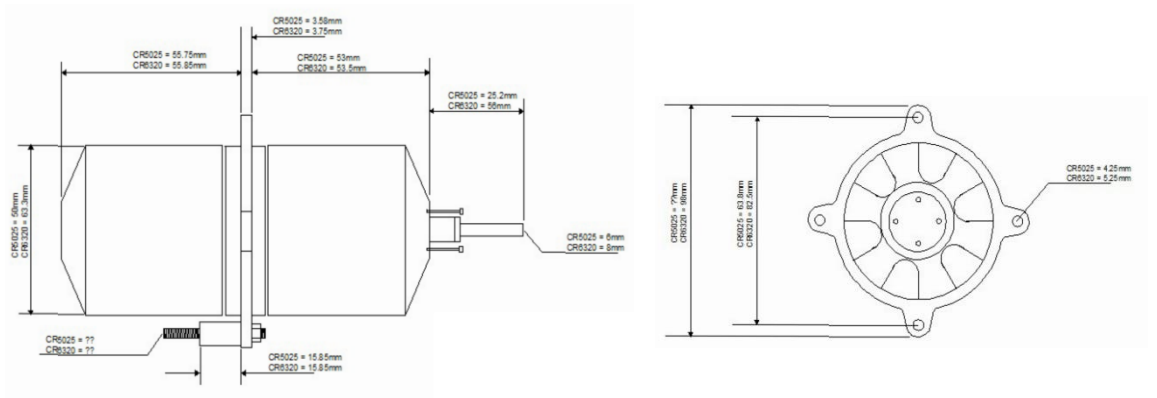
Dimensionszeichnung Himax Contra-Rotating Motor [2]
